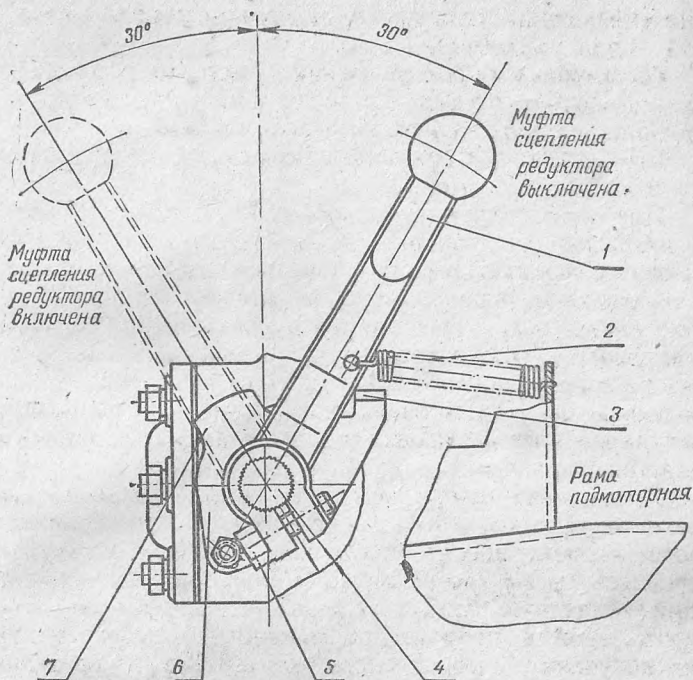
Регулировка муфты сцепления редуктора пускового двигателя:
